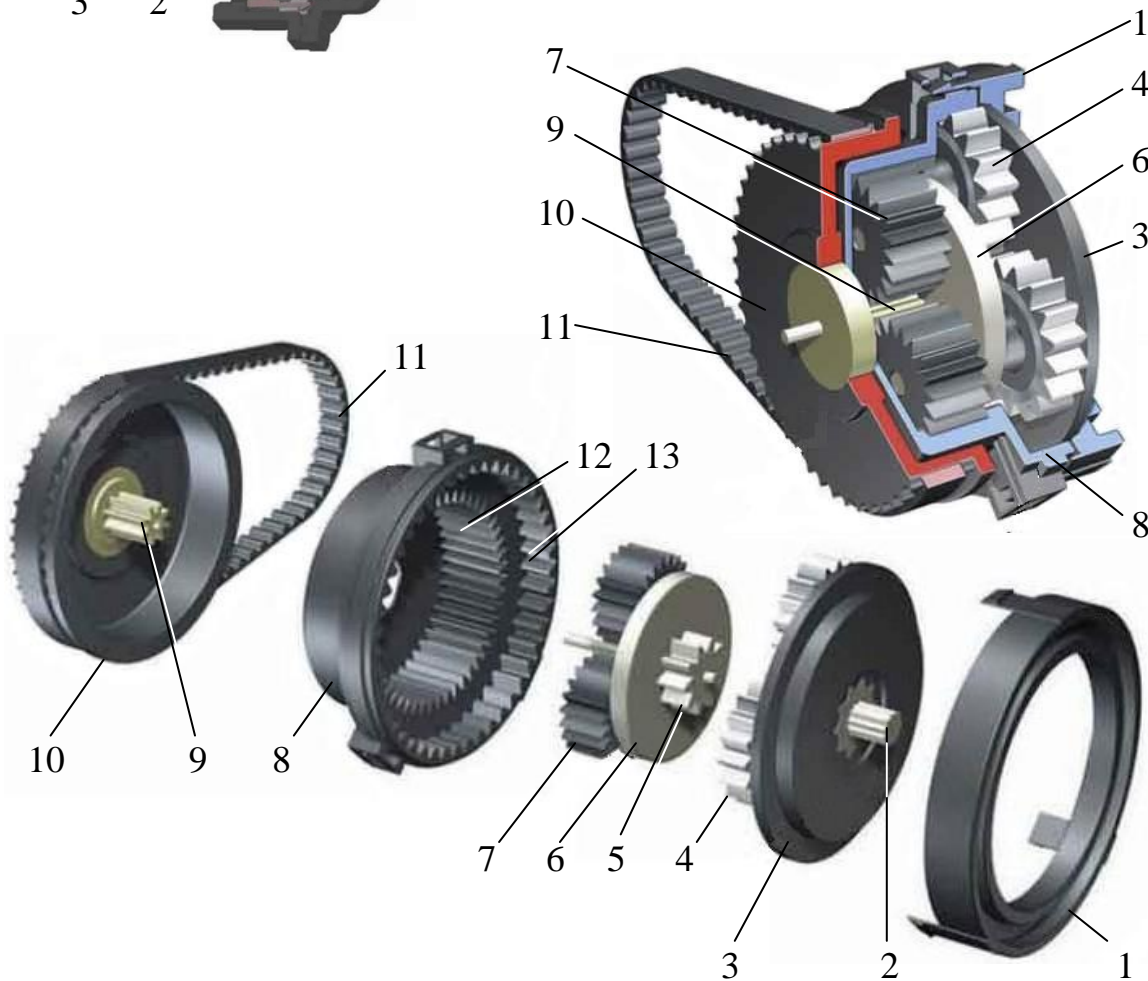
Конструкция планетарного редуктора привода электромеханического стояночного тормоза: 1 – крышка редуктора с фиксаторами; 2 – выходной вал редуктора; 3 – водило второго планетарного ряда; 4 – сателлиты второго планетарного ряда; 5 – солнечная шестерня второго планетарного ряда; 6 – водило первого планетарного ряда; 7 – сателлиты первого планетарного ряда; 8 – корпус редуктора; 9 – солнечная шестерня первого планетарного ряда; 10 – первичная шестерня редуктора; 11 – зубчатый ремень; 12 – эпицикл первого планетарного ряда; 13 – эпицикл второго планетарного ряда
